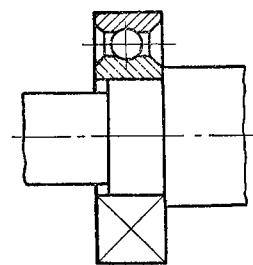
Допускаемое изображение подшипника в разрезе
